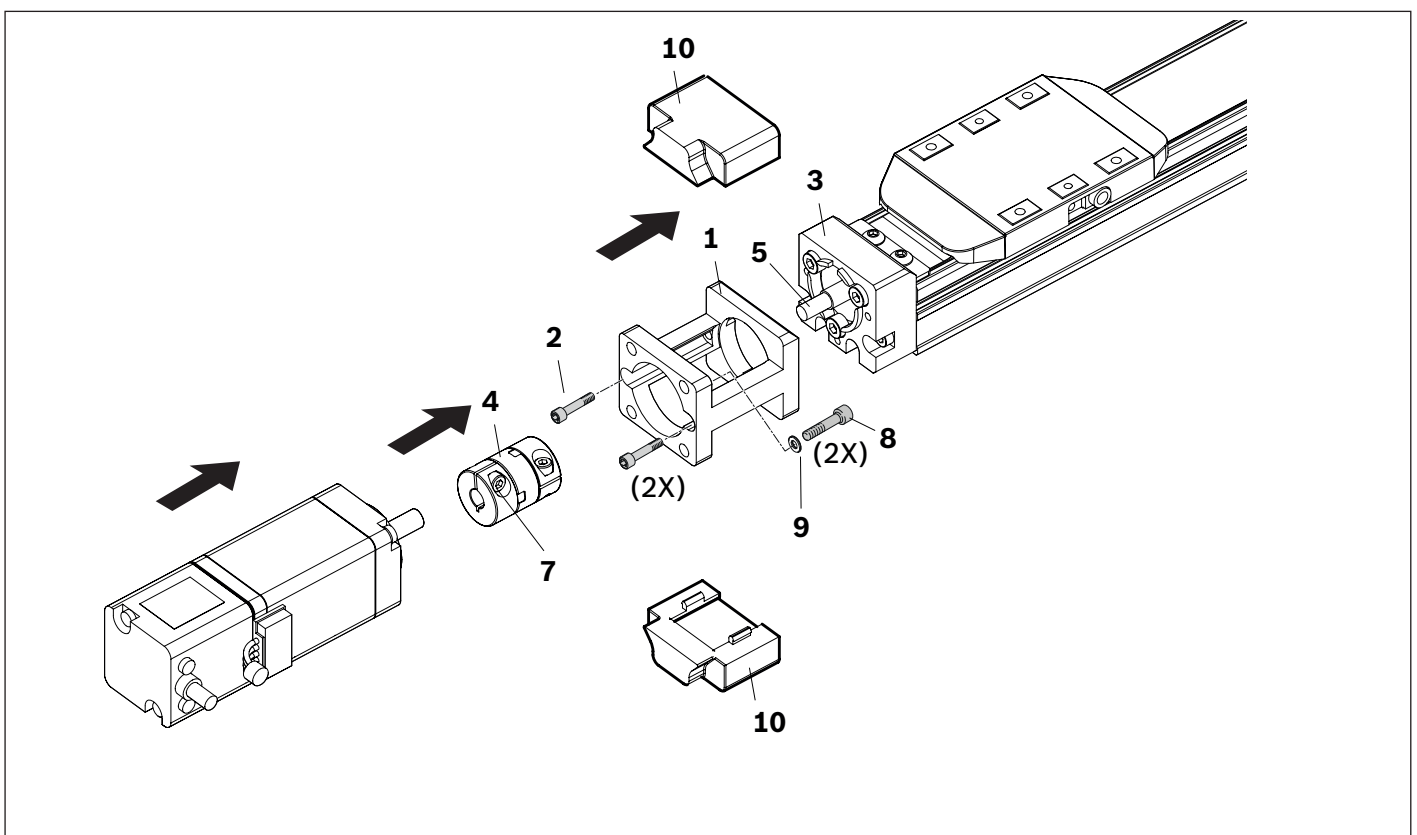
Motor mit Flansch und Kupplung montieren (SMS-030)
